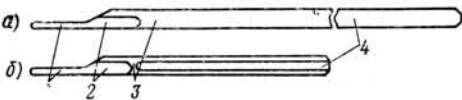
Самоудлиняющаяся ампула конструкции ИГД им. А. А. Скочинского: 1 — корпус ампулы; 2 — обратный клапан; 3 — отросток; 4 — подворотная часть ампулы
